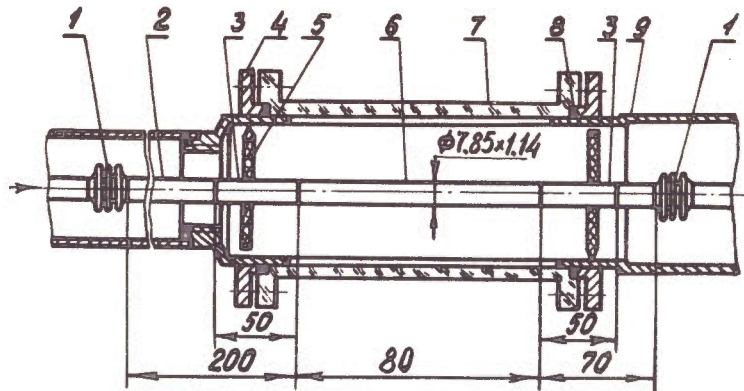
Узел для исследования структуры потока двухфазного гелия: 1 - сильфон; 2 - трубка из стали 12X18H10T; 3 - трубка из ковара; 4 - фланец; 5 - центрирующая вставка; 6 - трубка из молибденового стекла; 7 - корпус из органического стекла; 8 - резиновая прокладка; 9 - вакуумный корпус.
